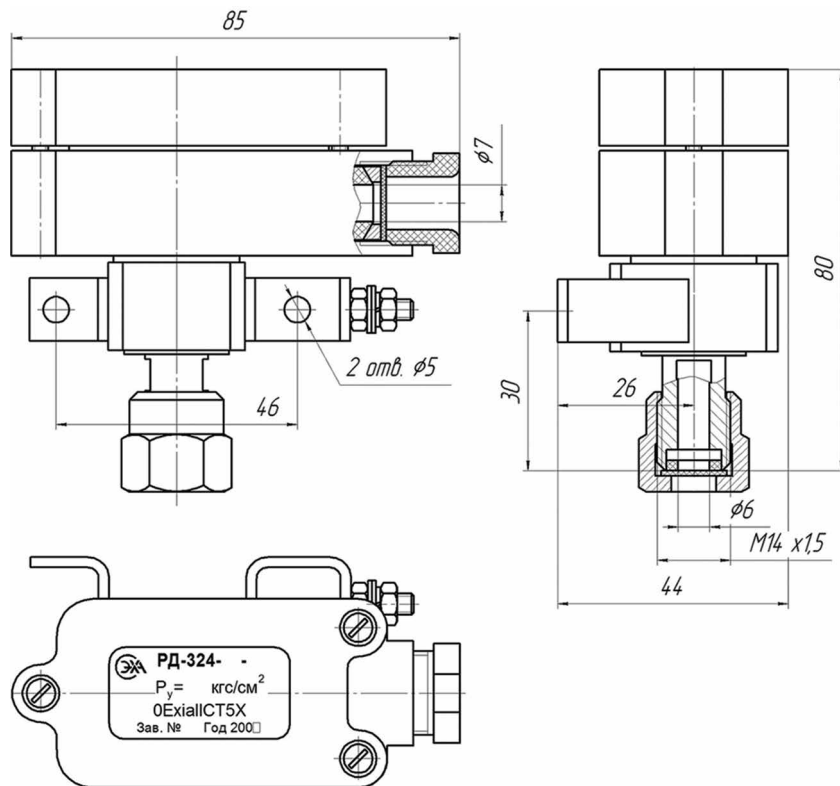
Габаритные и установочные размеры реле давления РД-324
